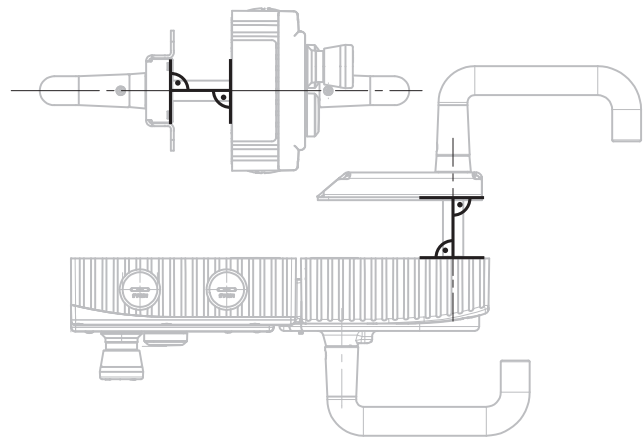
Montagebeispiel für rechts angeschlagene Tür (Übersichtsdarstellung)
